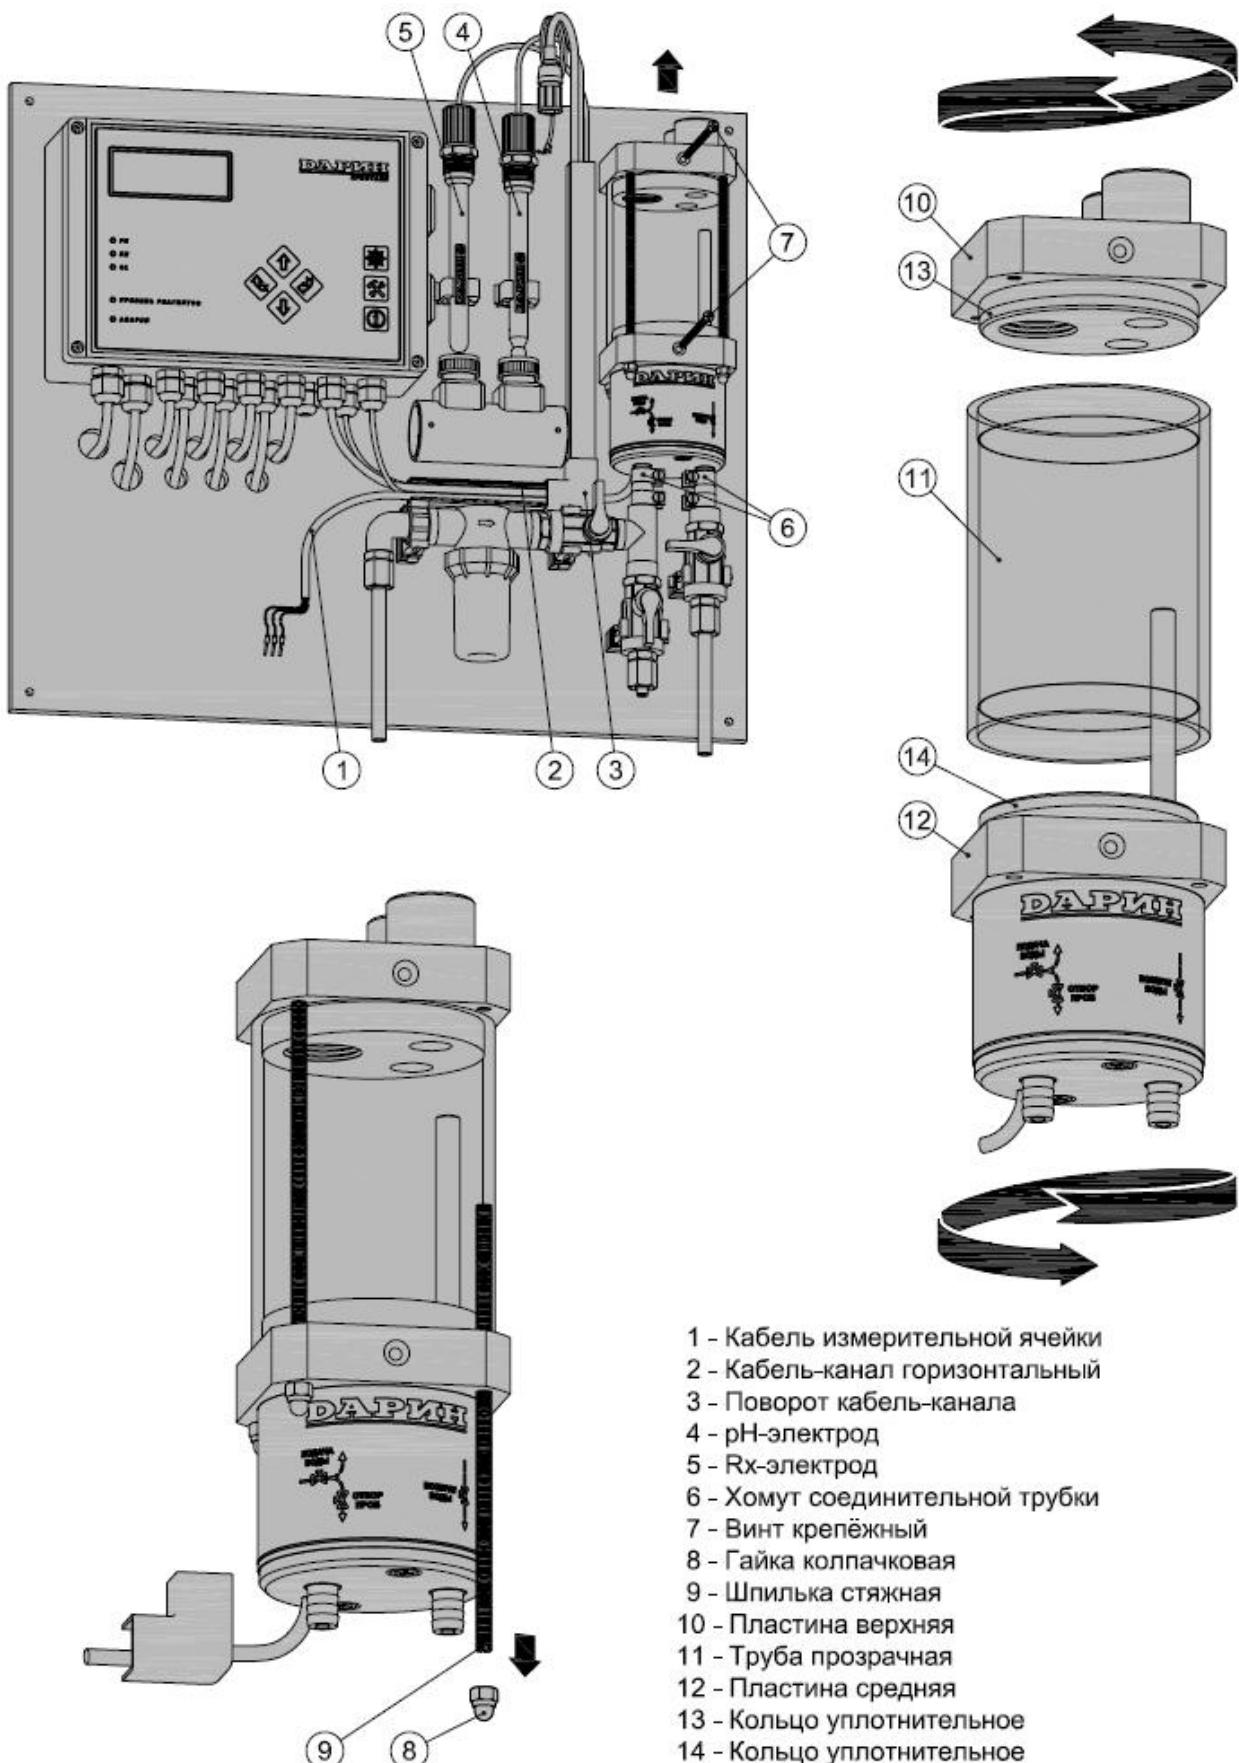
Очистка стенок проточной камеры измерительной ячейки
